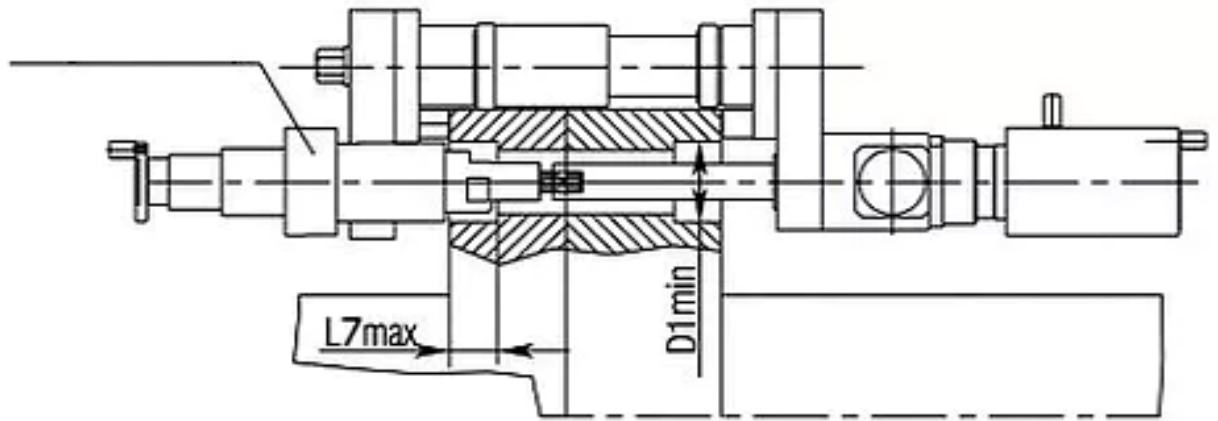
Прецизійний мобільний токарний верстат KDM
